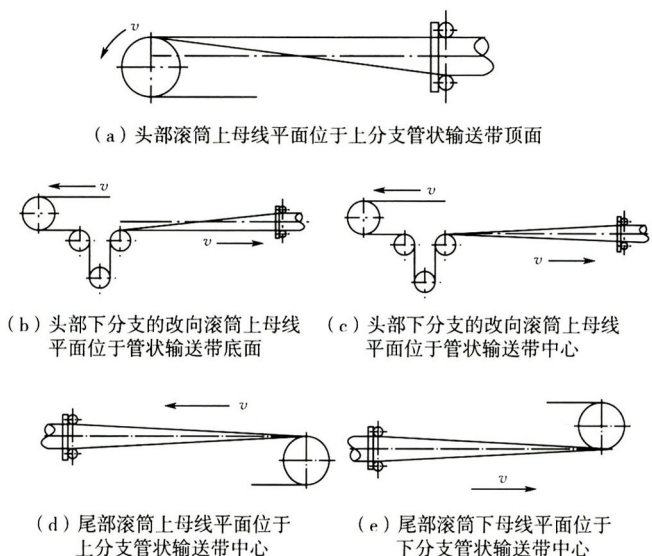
滚筒母线平面与管状输送带的相对位置示意图
